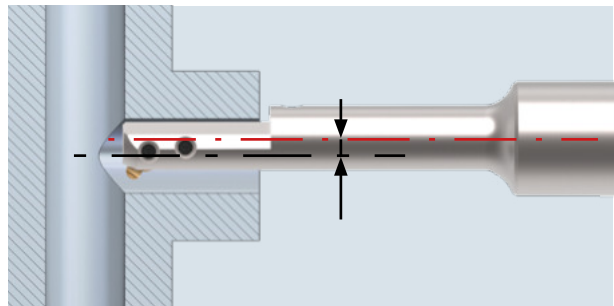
Die Entgratung des T-Stücks erfolgt durch die Querbohrung.
